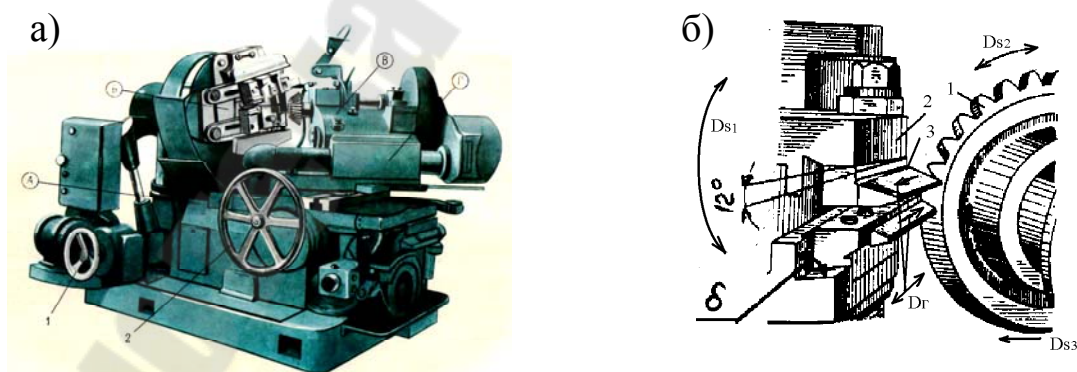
Общий вид зубострогального станка (а) и схема обработки зубьев прямозубых конических колес (б)
